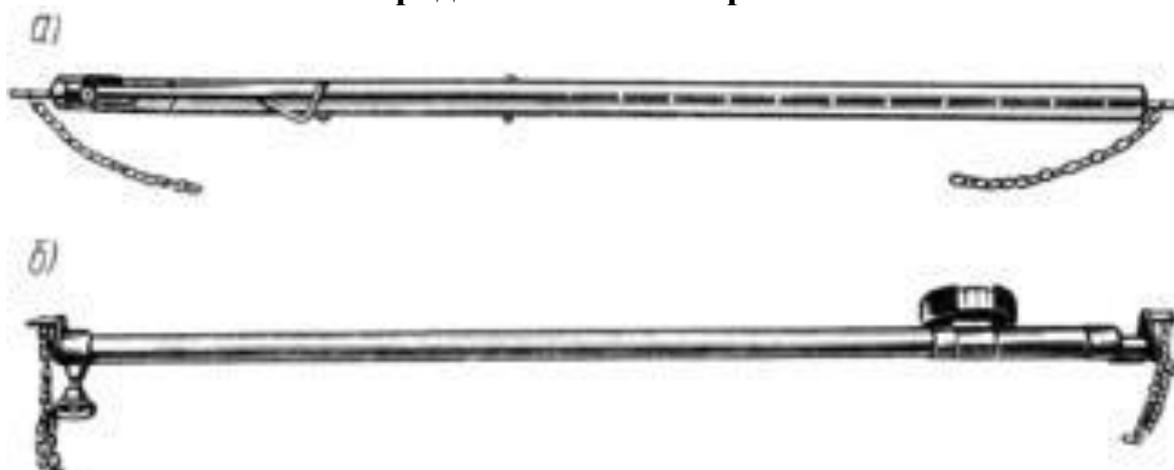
Линейка для проверки схождения передних колес автомобилей модели
